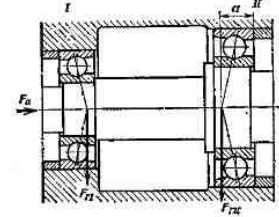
Схема установки радиально-упорных роликоподшипников в ступице колеса
